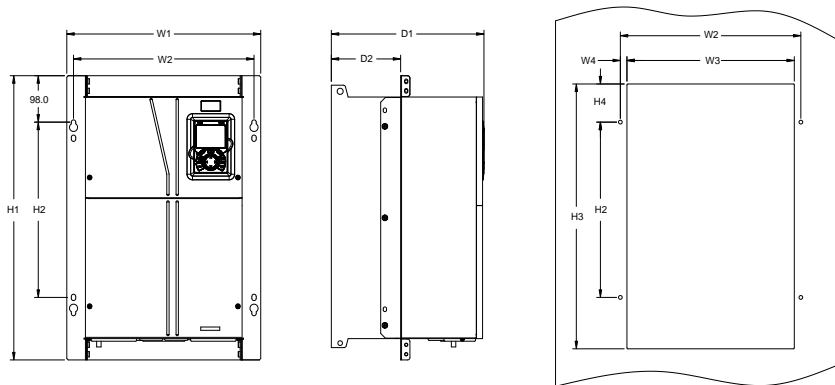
Схема ПЧ фланцевого монтажа 660 В, от 22 до 132 кВт
